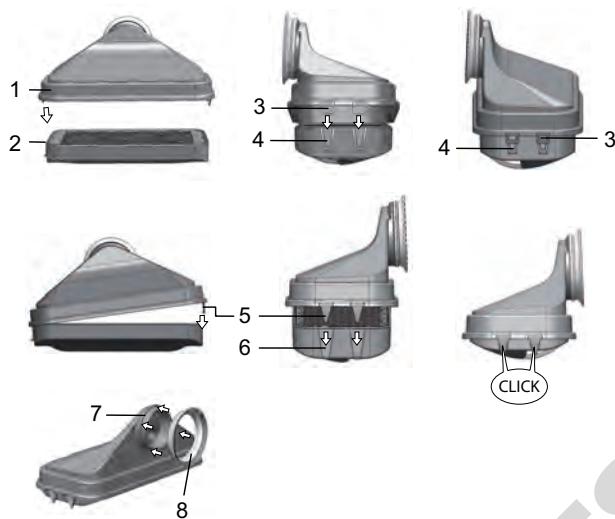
Assembler le filtre HEPA et le boîtier de filtre à air
